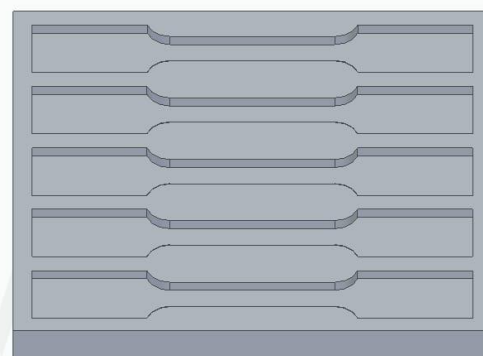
Molde completo de acordo com a área de impressão da impressora 3D.
